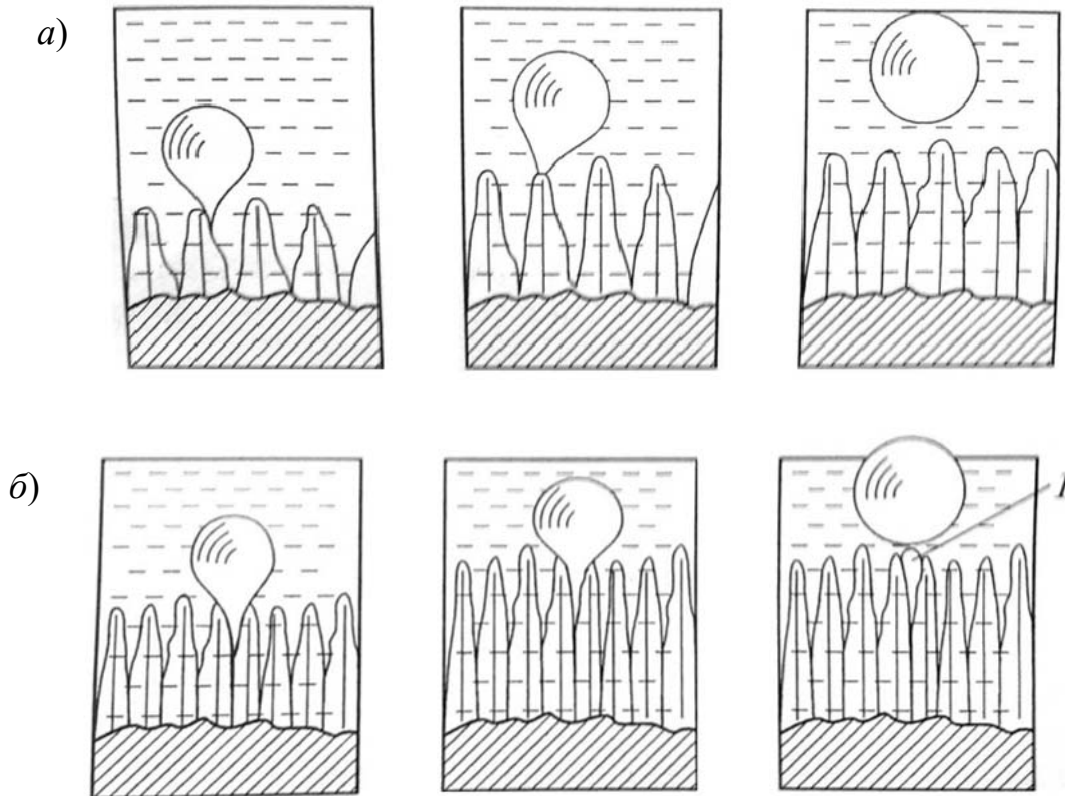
Схема формирования газового пузырька и его отрыва от фронта кристаллизации металла шва при малой (а) и большой (б) скоростях сварки (1 – остаток газового пузырька внутри металла)
